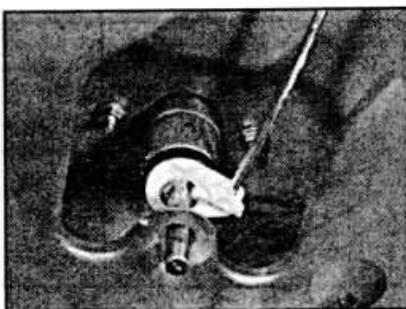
Расположение стопорных гаек крепления цилиндра замка.
